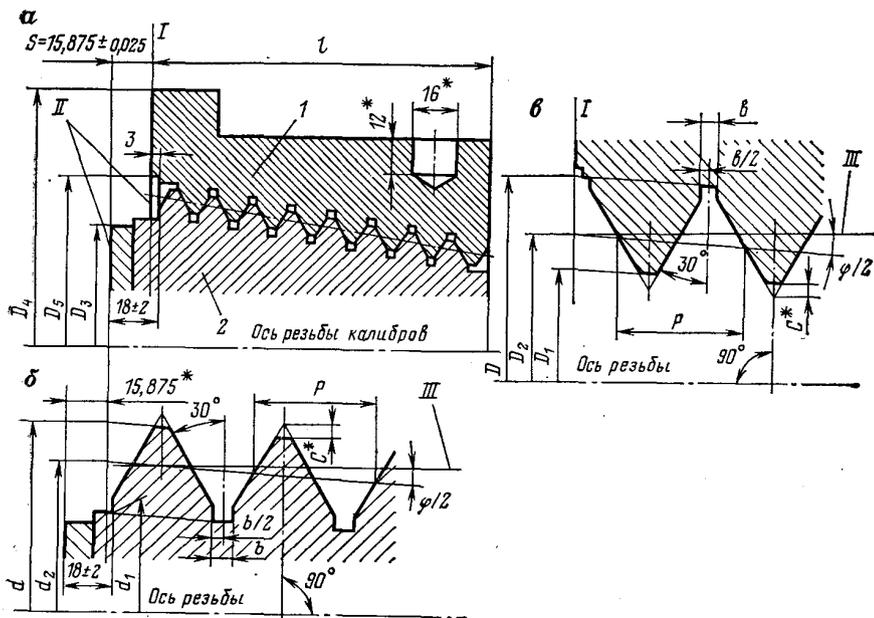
Калибры для контроля замковой резьбы по ГОСТ 5286—75:
